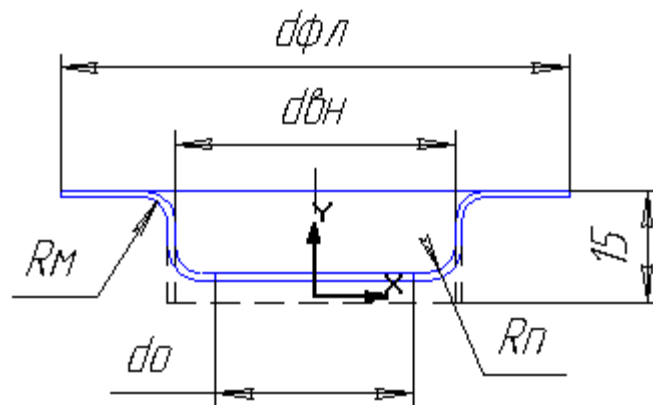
Схема попередньої витяжки і відбортовки
